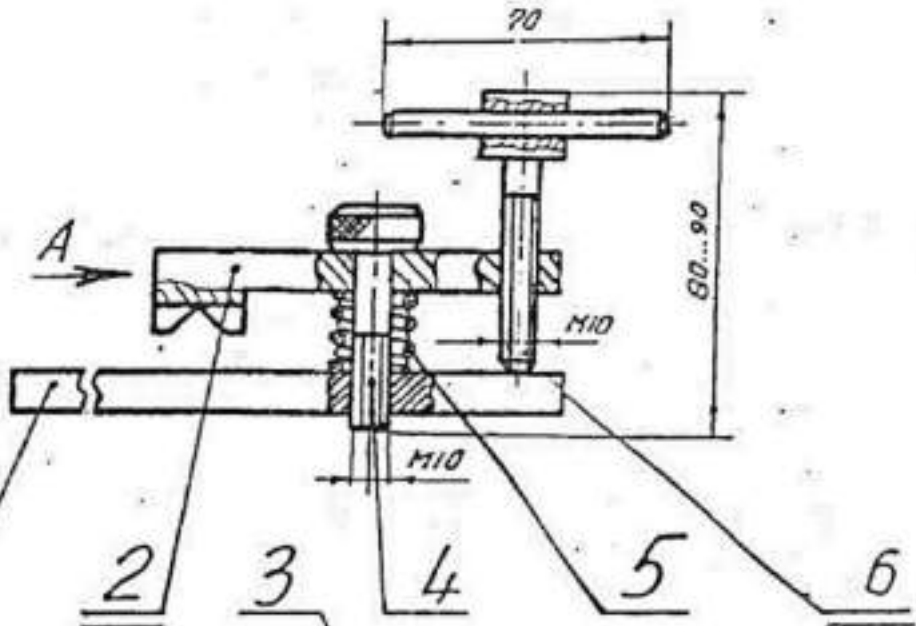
Пример листа 2-3. Сборочный чертеж
